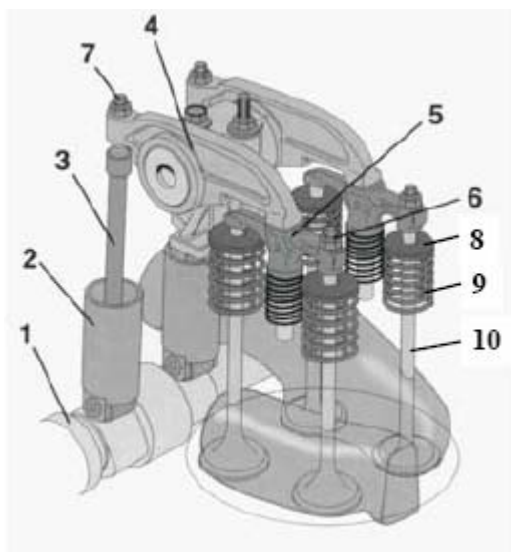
Rozdělení dle uspořádání ventilových rozvodů s mechanickým ovládním [2]
